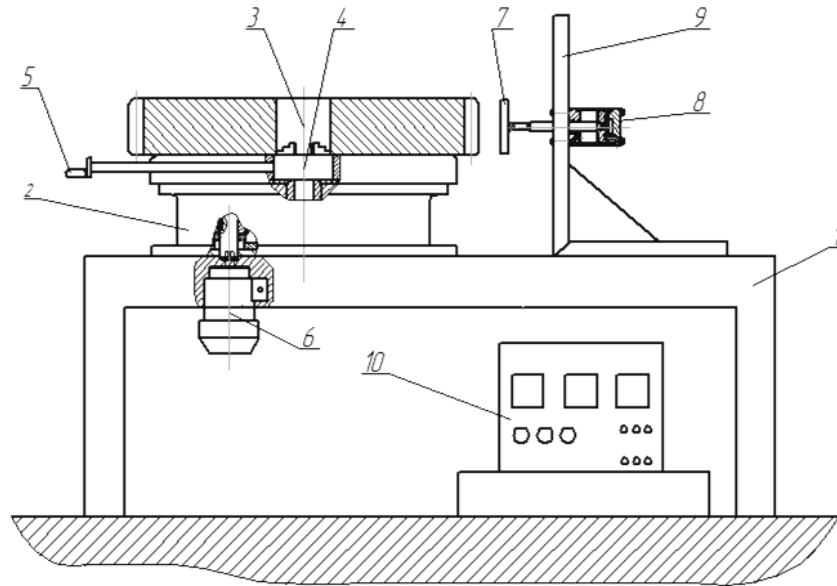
Схема промислової установки для МІО зубчастих коліс
